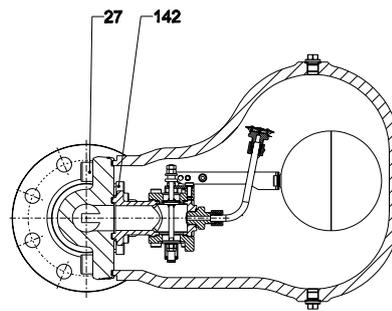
1 mit Flanschen - horizontale Einbaulage
